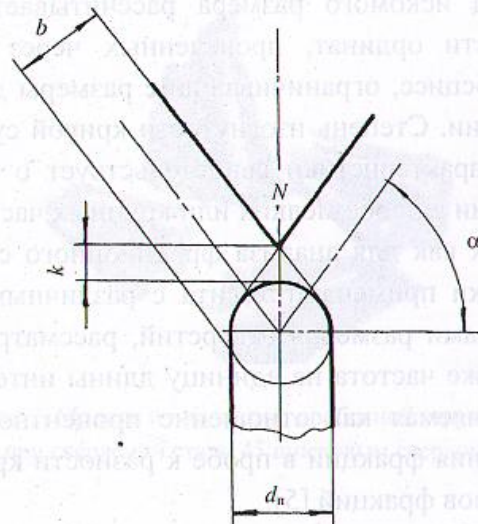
Схема подрезания периодического профиля кулачка при его фрезеровании концевой фрезой
